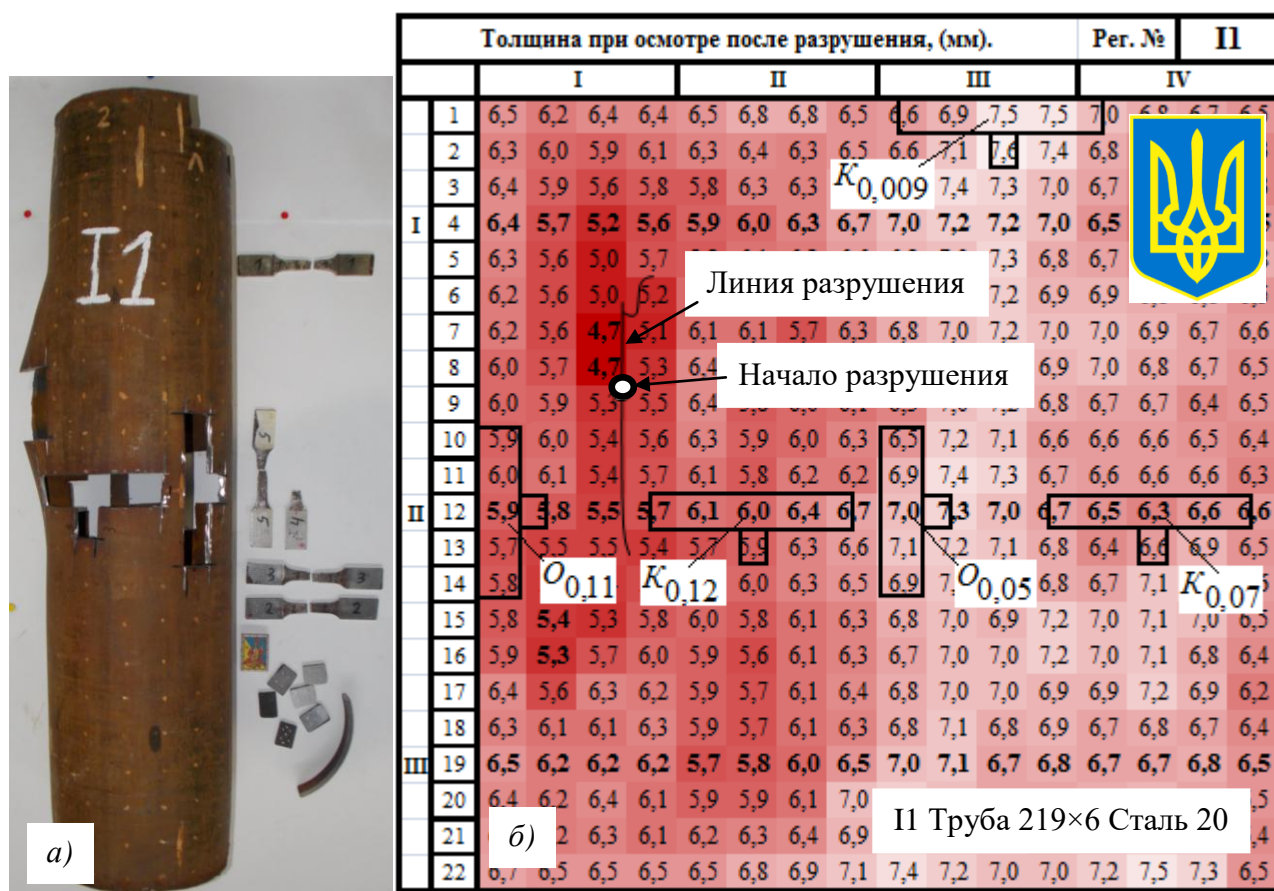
Схема вырезки и обозначения заготовок образцов на растяжение и для замеров твердости из цилиндрической гильзы с днищами разрушенной внутренним давлением, (II, сталь 20):
